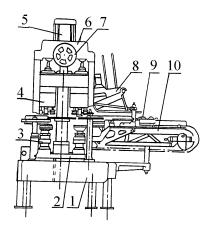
Автоматическая закаточная машина K3C-12: 1 — станина; 2 — закаточная карусель; 3 — шпиндель нижнего патрона; 4 — закаточная головка; 5 — электродвигатель; 6 — редуктор; 7 — механизм для ручного проворачивания машины; 8 — механизм подачи крышки; 9 — распределитель банок; 10 — загрузочное устройство
